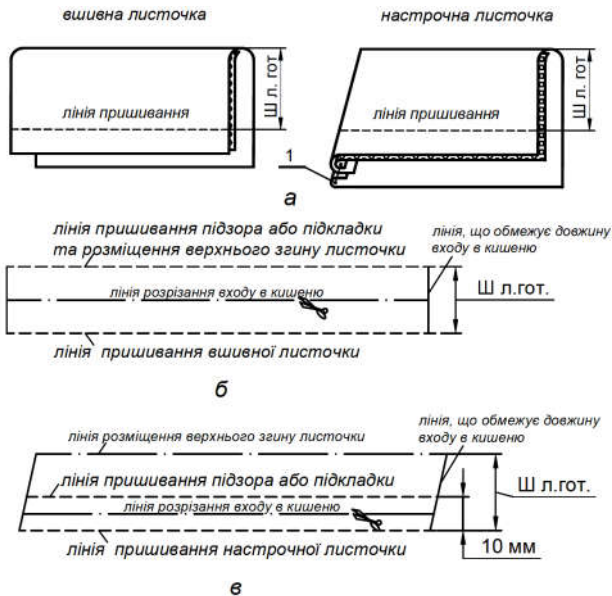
Початкове оброблення листочок (а) та підготовка основної деталі до монтажу прорізних кишень з вшивними (б) і настрочними листочками (в)
